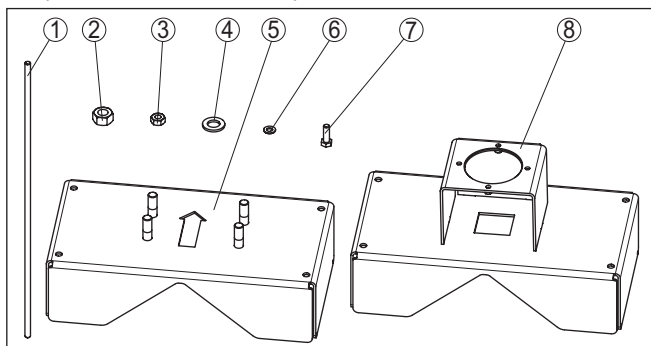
Dispositif de fixation pour conduites traversées perpendiculairement KV 31, Montage horizontal du capteur
